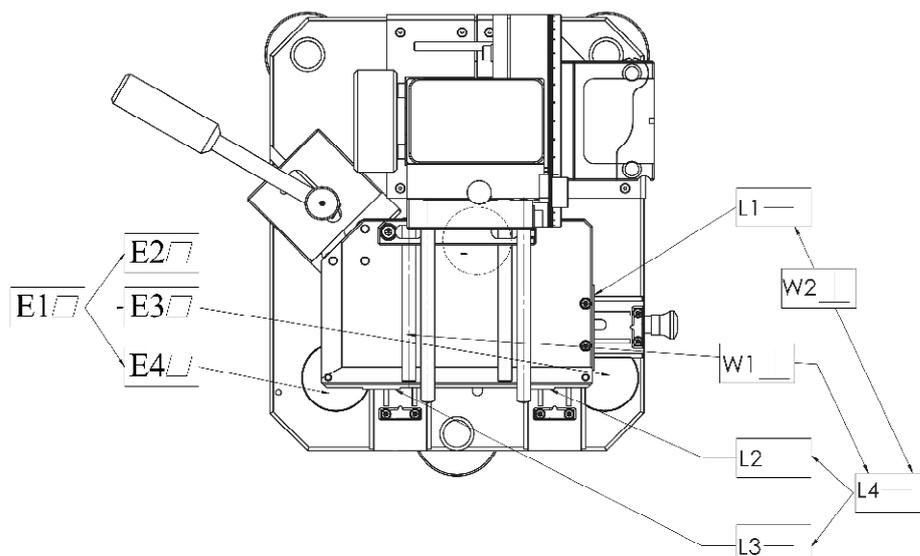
Чертеж установки для поверки систем лазерной центровки PRÜFTECHNIK CALI-CHEK F. Вид сверху
